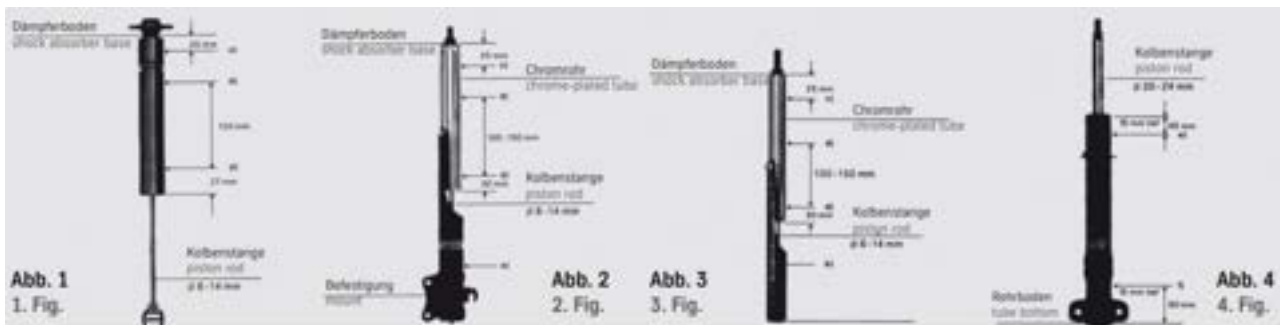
Amortizoarele BILSTEIN bitubulare cu gaz sub presiune, diametrul tijei pistonului 20-24 mm (se îndepărtează accesoriile, tubul de protecție sau burduful) sunt fixate pe o bază adecvată, de exemplu într-o prismă, și perforate central în cele două poziții care trebuie găurite conform desenului 4. În primul rând, amortizorul trebuie găurit în apropierea garniturii tijei pistonului cu un burghiu de 5 mm, astfel încât azotul gazos să poată ieși (e), continuați găurirea la o adâncime de 15 mm (e). Efectuați a doua gaură în poziția specificată (f), (la 80 mm de fundul tubului, cu tija pistonului extinsă) la o adâncime de 15 mm pentru a permite scurgerea uleiului. Prin mișcarea de mai multe ori a tijei pistonului, uleiul este pompat afară din tubul amortizorului și colectat într-un recipient omologat.
